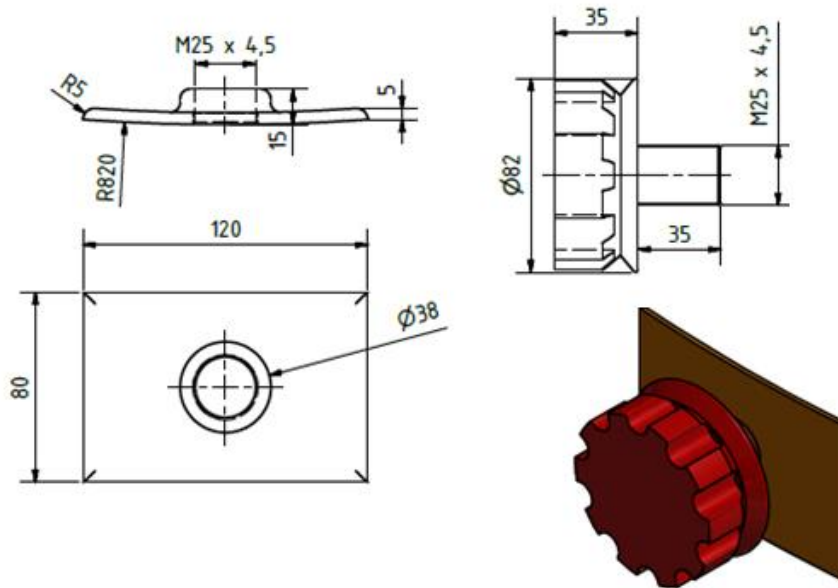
Dibujo técnico de piezas para el cierre del estanque.
